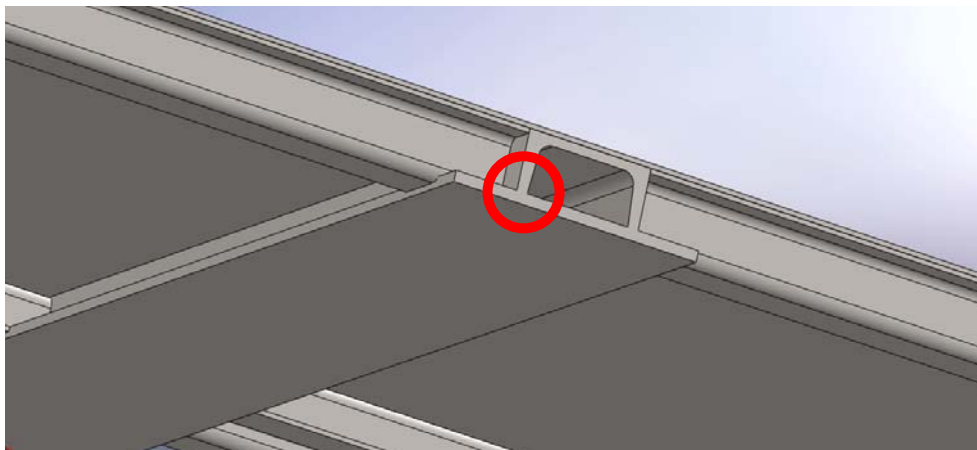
Detalle perfil UPN recortado para soldar con placa
